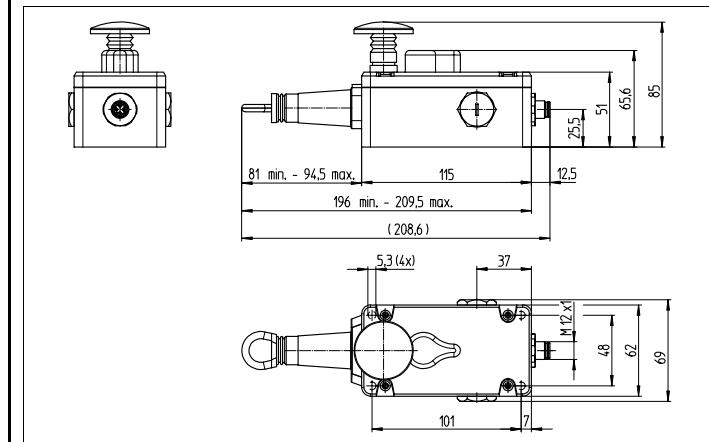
disegno quotato dell'interruttore a fune i150-RP224 (mm)
